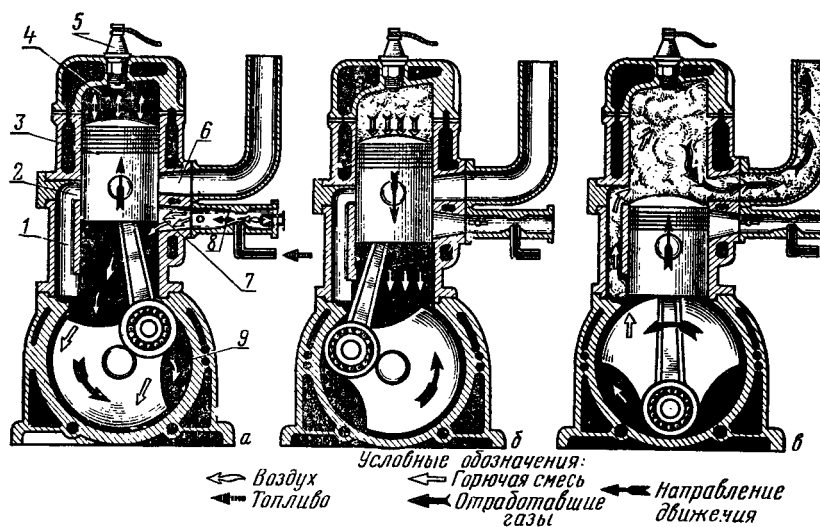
Схема устройства и работы двухтактного карбюраторного двигателя:
